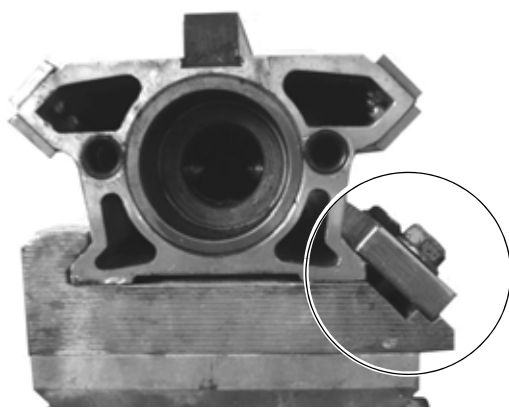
Направляющий рельс закреплен на поворотной колодке правильно
